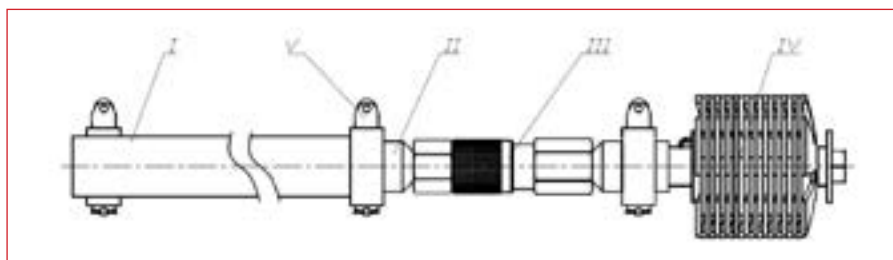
Схема дефектоскопа: I – полая транспортирующая штанга; II – резьбовой переход; III – БРС; IV – токопроводящая резина; V – ролик
